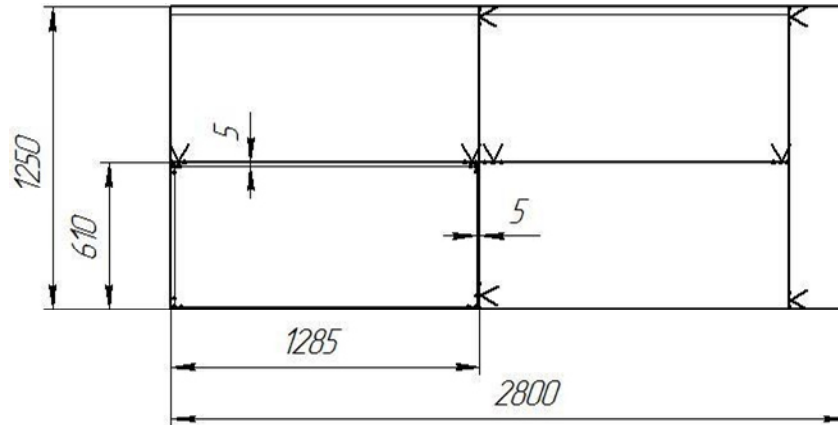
Ескіз розмітки заготівки на листі.
